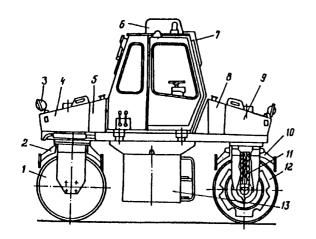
Общий вид дорожного самоходного катка ДУ-64:
